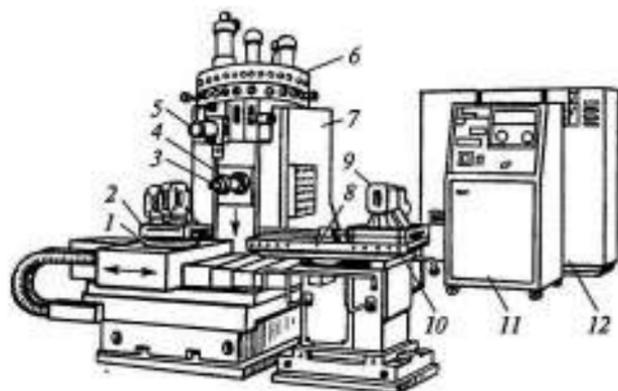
Горизонтальный многоцелевой сверлильно-фрезерно-расточный станок с ЧПУ:
